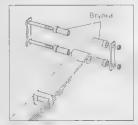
Листовые рессоры оборудованы резиновыми втулками
